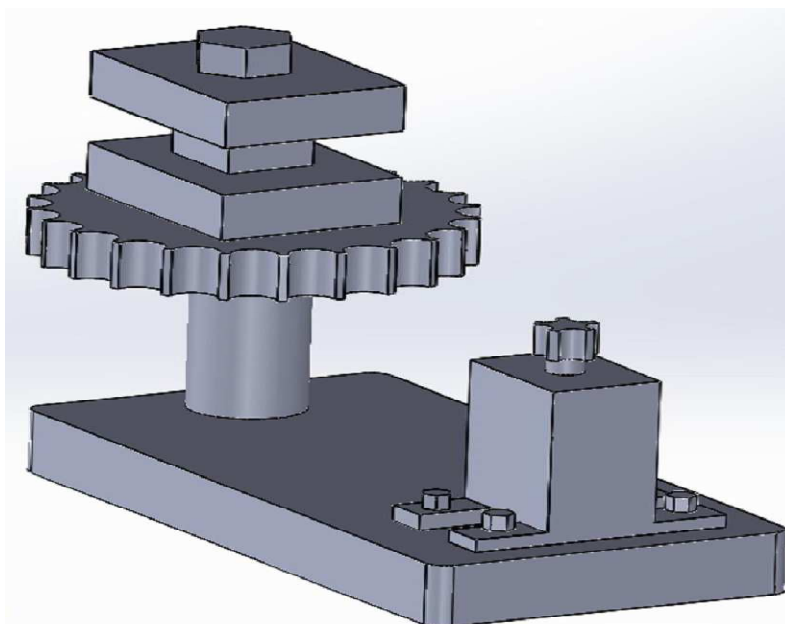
couple d'engrenage à installer sur la boîte des vitesses
